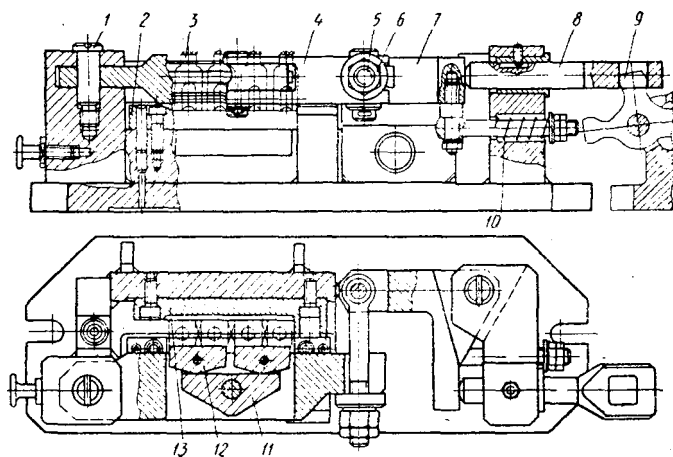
Многоместное фрезерное приспособление с зажимом от универсального силового привода
